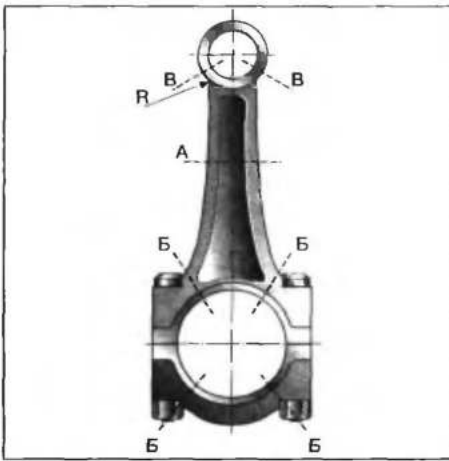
Опасные сечения шатуна: А — при гидроударе; Б — при разрушении шатунного подшипника; В — при перегреве головки из-за некавалифицированного монтажа поршня с пальцем
